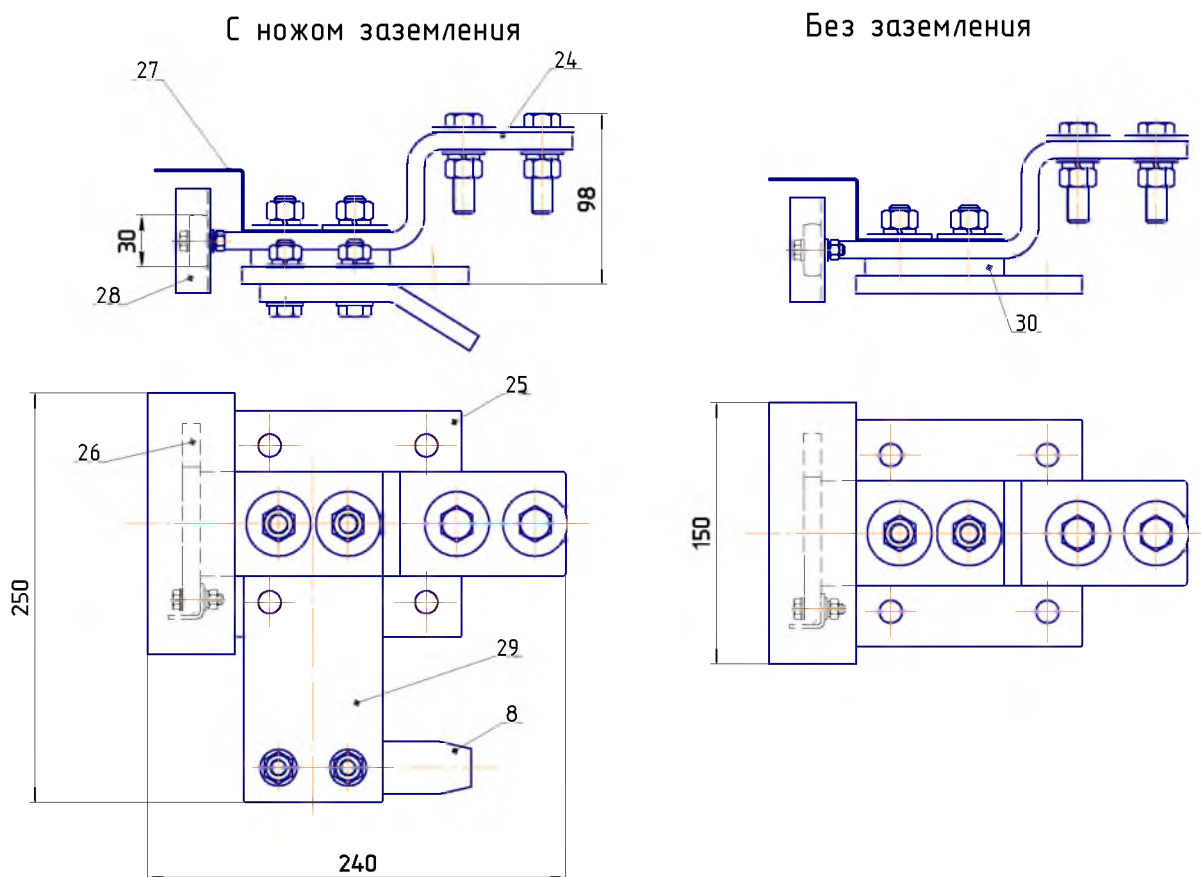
Неподвижный нож контактный разъединителя РГП СЭЩ[®]-35/1000
